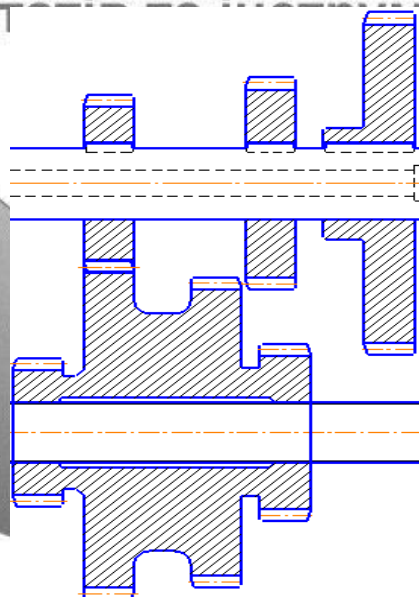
Конструктивна схема переміщення та положення блока зубчастих коліс Б3– зачеплення Z107/Z13.
